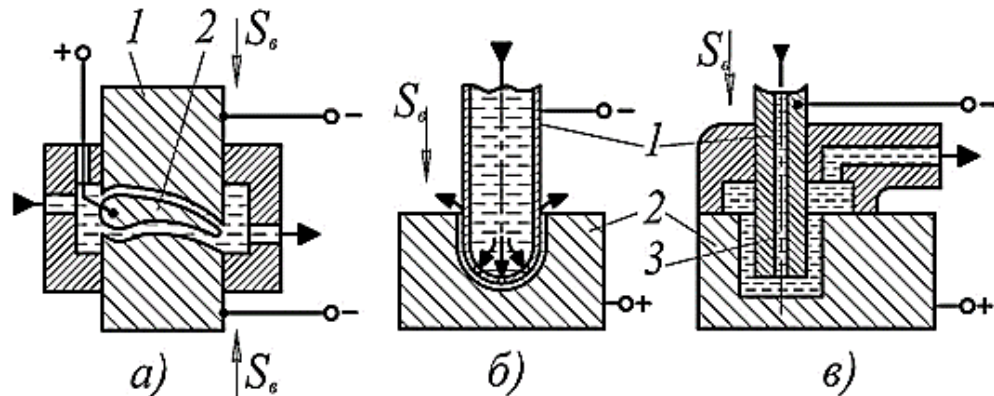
Схеми електрохімічної розмірної обробки:
